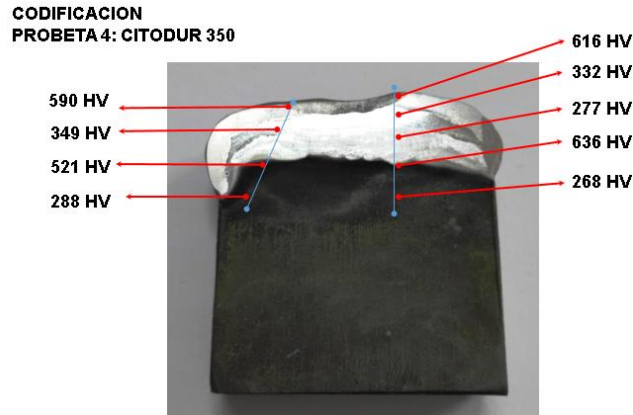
Probeta soldada con electrodo Citodur 350
